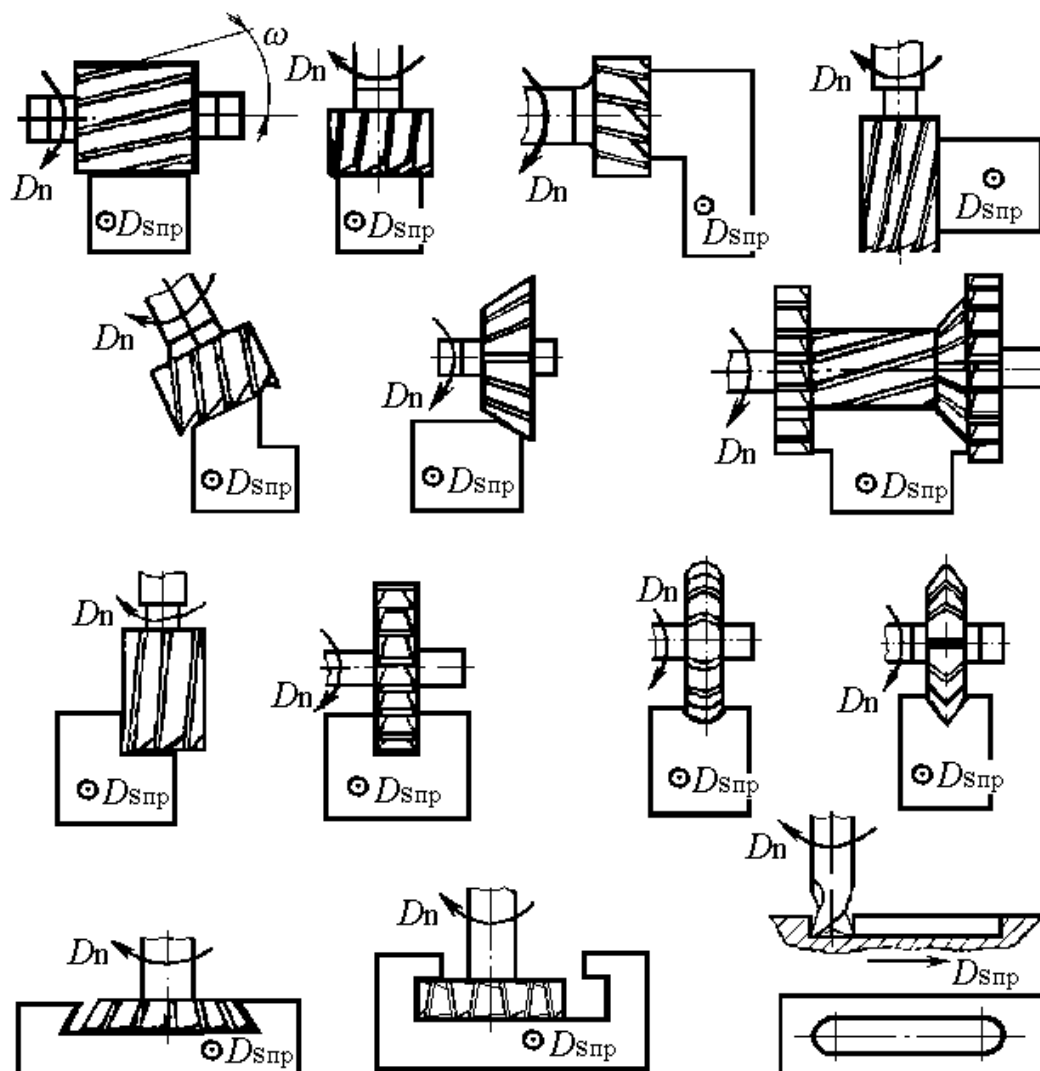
Основные виды фрез и работы, выполняемые на фрезерных станках
